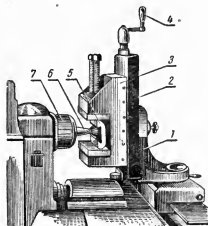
Универсальное приспособление для фрезерования мелких и средних деталей на токарном станке:
